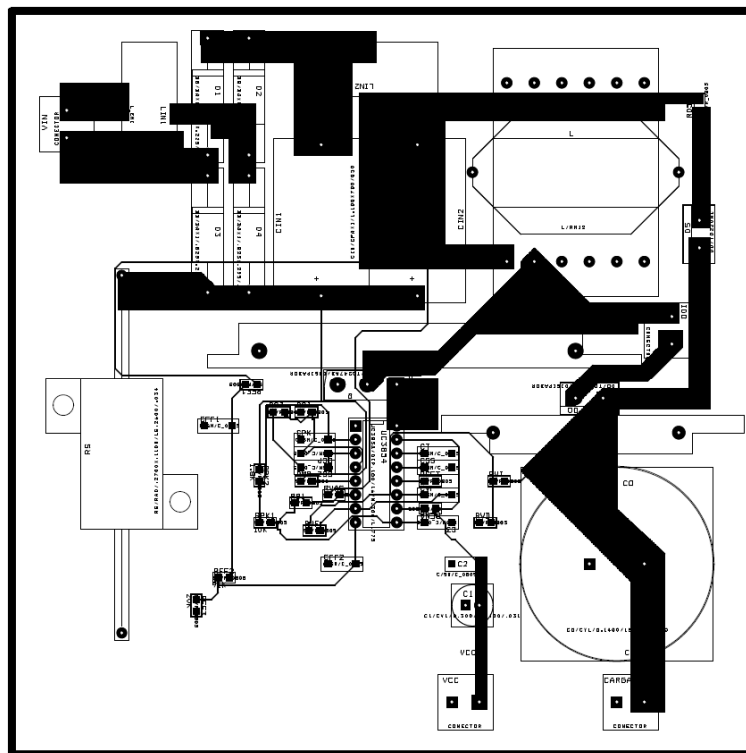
17 Placa PCB componentes colocados, borde de placa y rutado de pistas con áreas de cobre.
